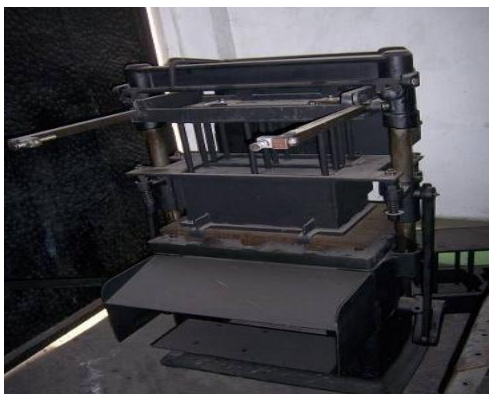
Máquina de vibro compactación Vibramatic V/3. Fuente [26].
